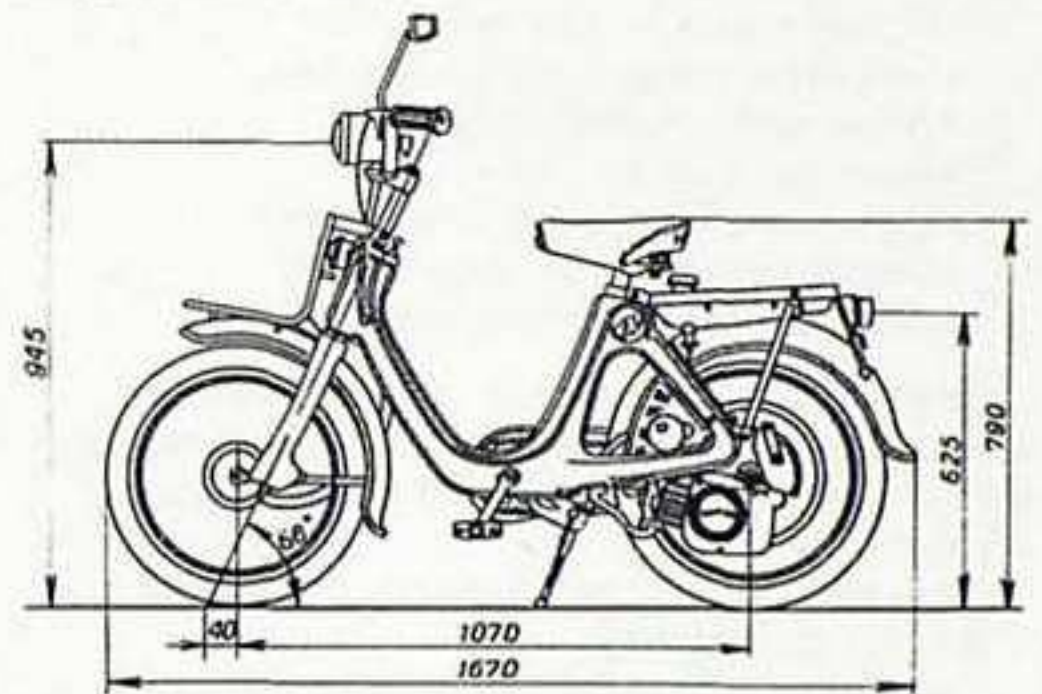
Общий вид и габаритные размеры мопеда P50.
